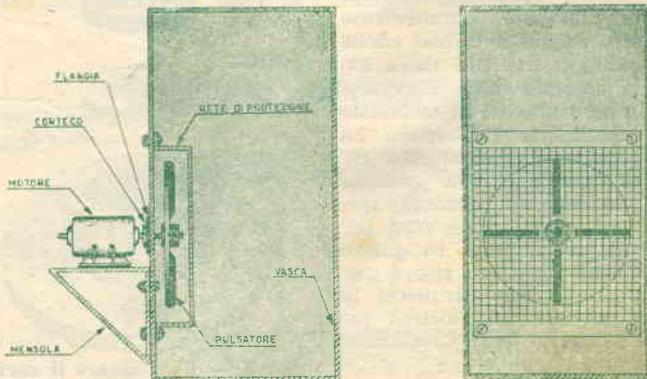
Due aspetti della lavatrice vista di lato e di fronte.
